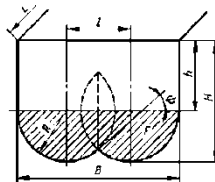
Схема корпусу змішувача із Z-подібними лопатями
